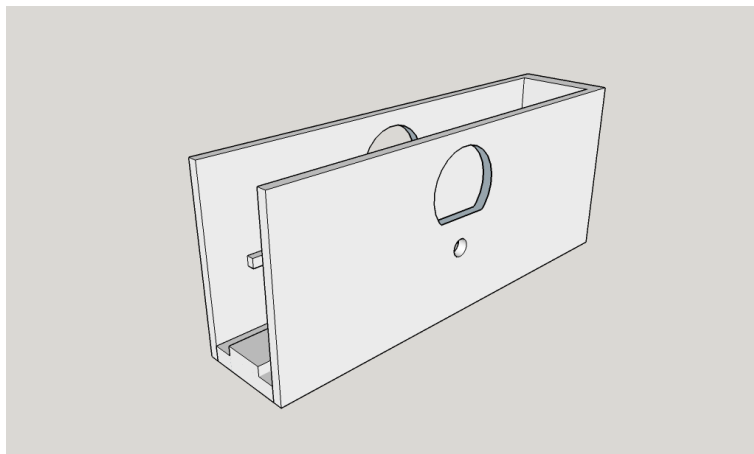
Calhas e Estrutura de Protecção desenhadas
